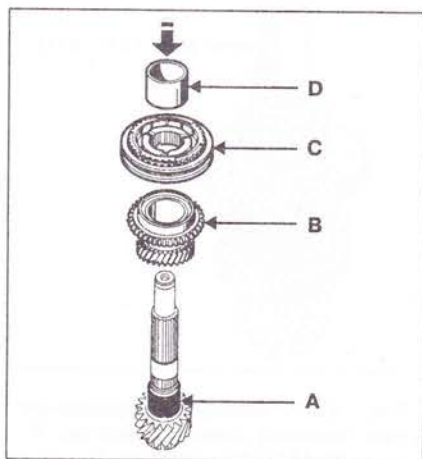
Установите игольчатый подшипник A, шестерню 6-й передачи B, ступицу зубчатой муфты 6-й/5-й передач C, втулку шестерни 5-й передачи D.
